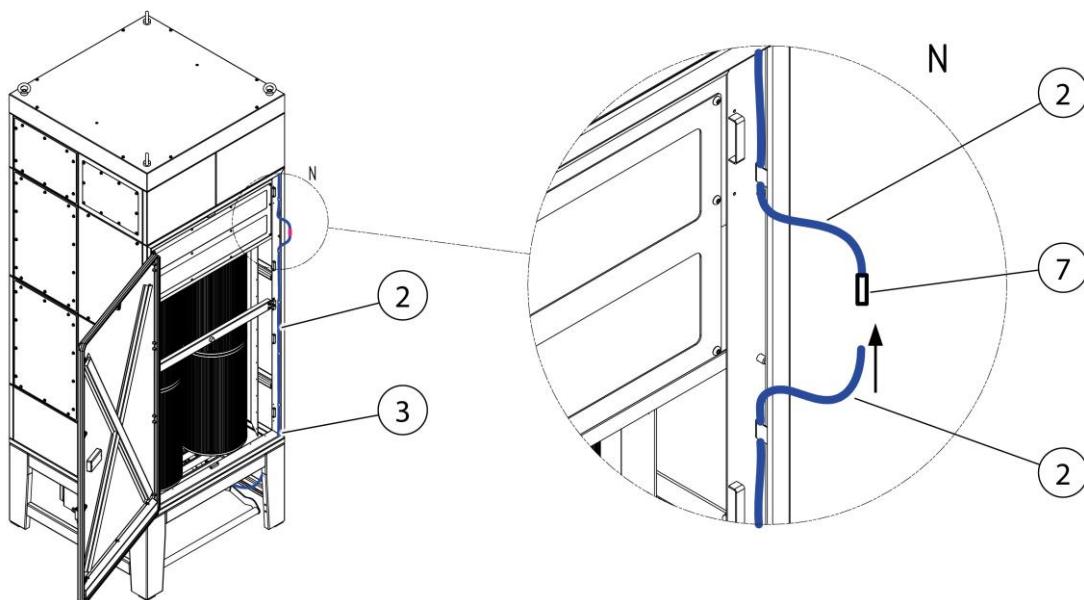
Монтаж - Прокладка шланга сжатого воздуха
